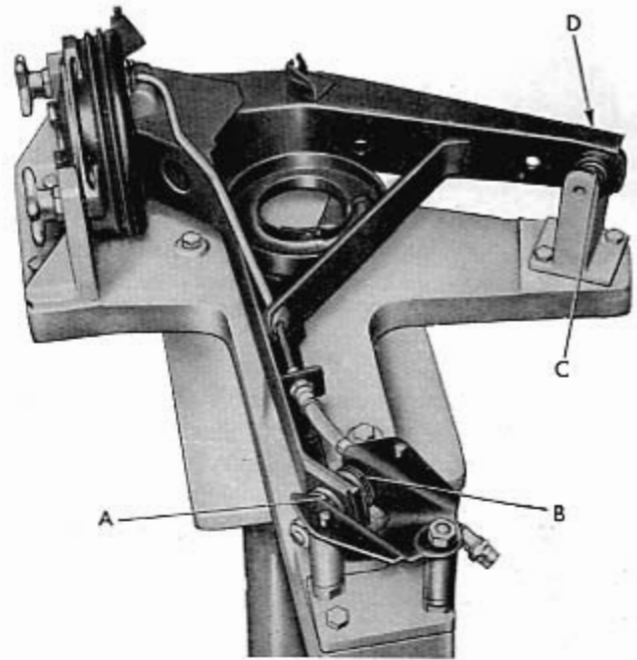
Réglage du bras oscillant arrière droit sur l'outil A. 66064.
